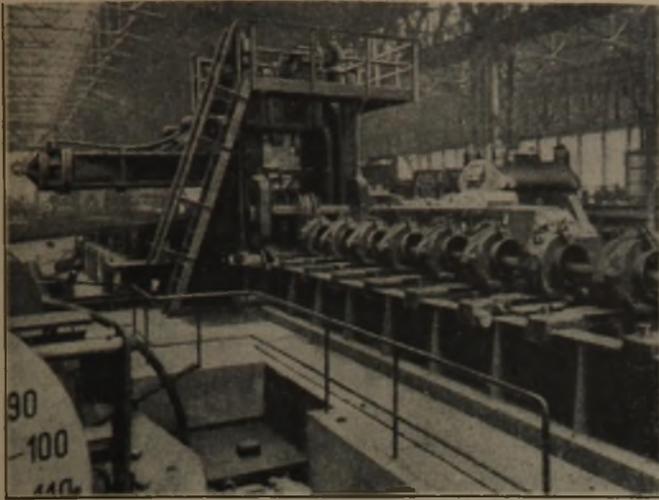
Automatisches Zweiwalzen-Rohrwalzwerk.
